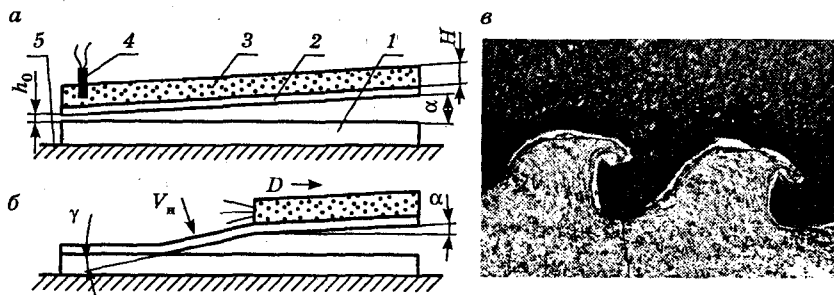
Схемы сварки взрывом (а, б) и микроструктура зоны соединения биметалла (сталь 40Х — Р6М5), полученного сваркой взрывом (в): 1 — нижняя плакируемая пластина; 2 — верхняя плакирующая пластина; 3 — ВВ (взрывчатое вещество); 4 — ЭД (электродетонатор); 5 — основание
